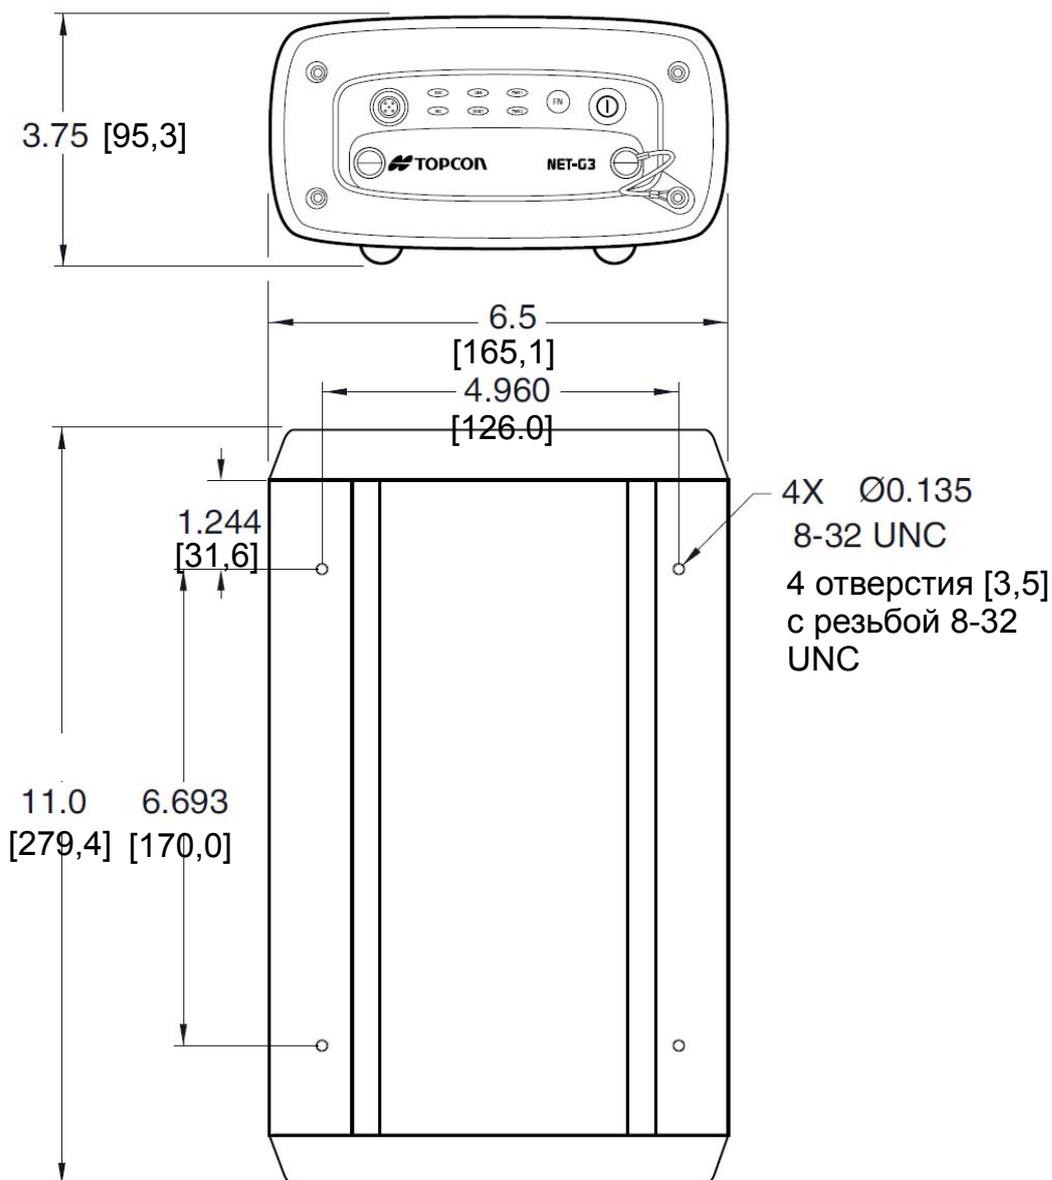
Габаритный чертеж приемника NET-G3
